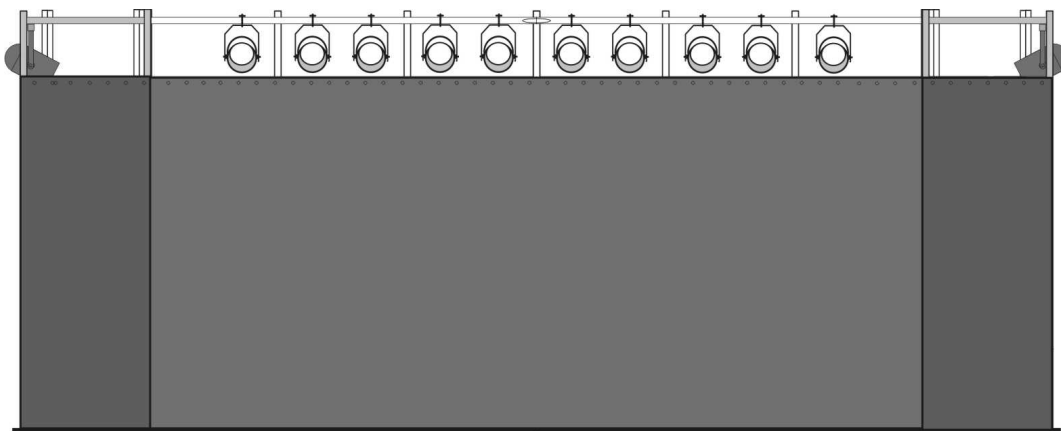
Vista frontal de la cámara terminada, con iluminación instalada.
